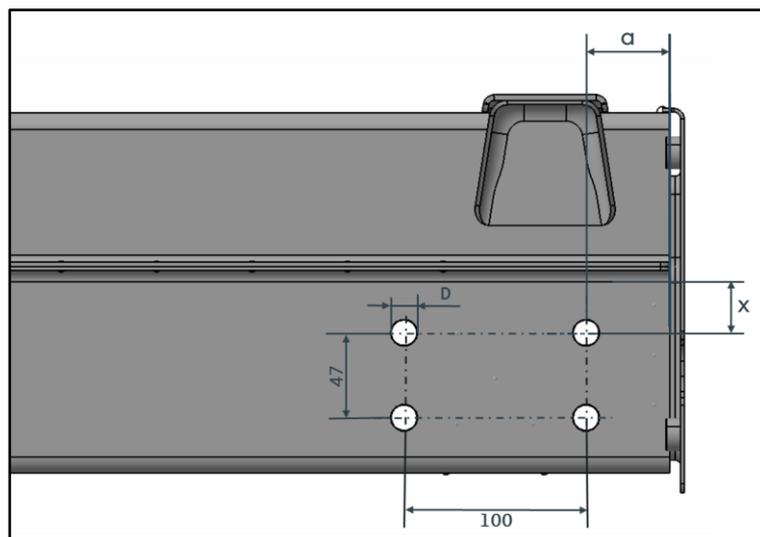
Châssis/plateau 3,0 à 5,5 t
